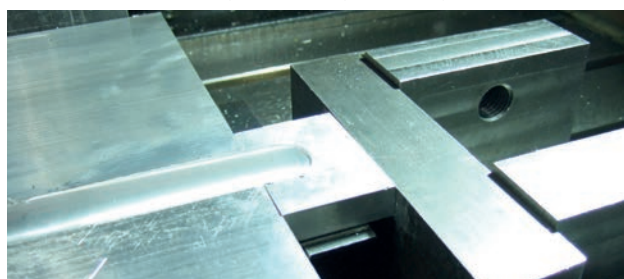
Накладная пластина в начале сварочного шва
